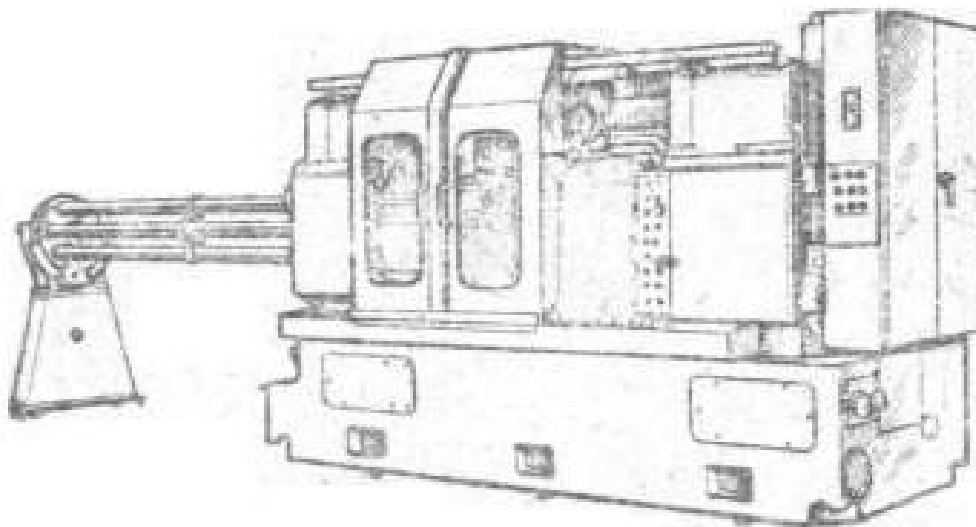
Автомат токарный шестишпиндельный прутковый горизонтальный мод. 1Б240-6(6К)
